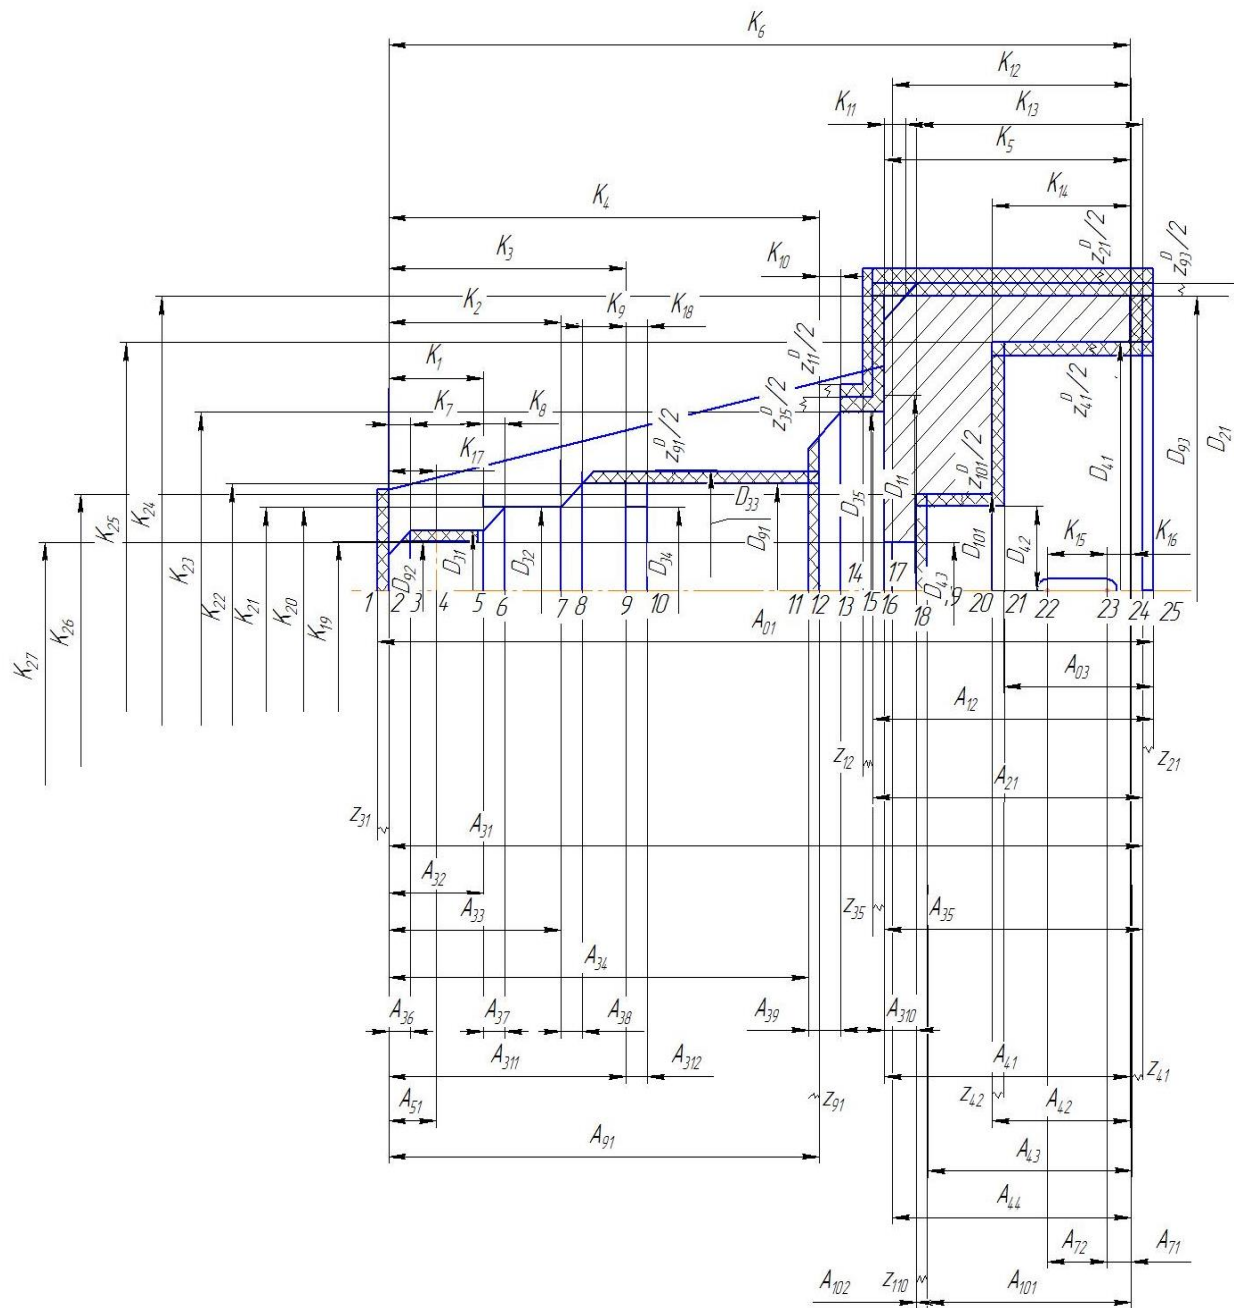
Размерная схема изготовления выходного вала.
